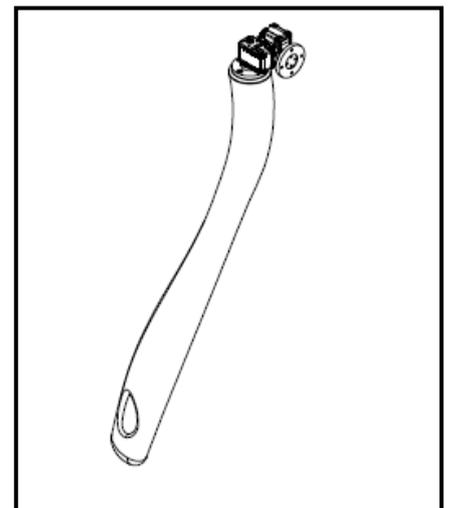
Vista isométrica del Brazo (Fuente: Propia)
